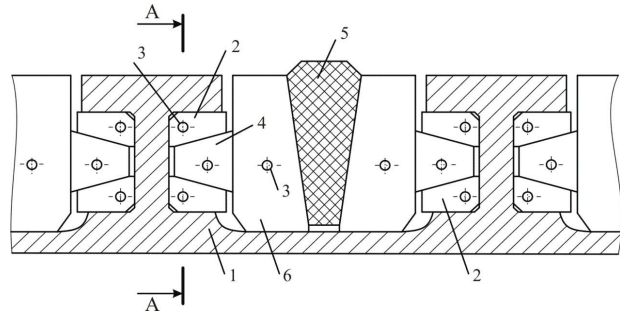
Оправка для гибки панелей с Т-образными выступами
